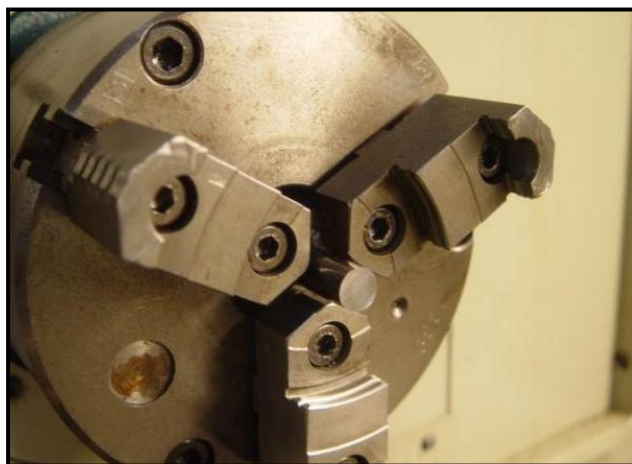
Detalhe do tarugo preso a castanha do torno antes da usinagem
